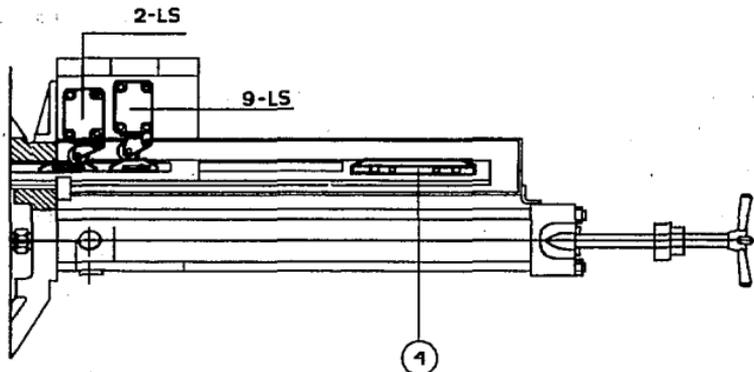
PROTECCION DEL MOLDE VISTA TRASERA.
